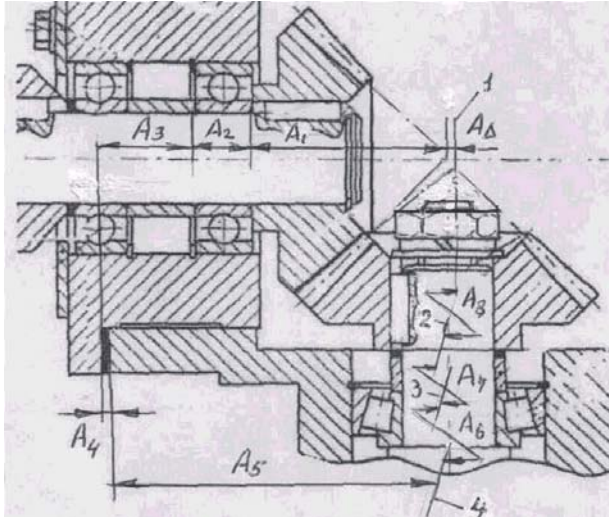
Схема размерной цепи A_{Δ} , определяющей совпадение вершин делительных конусов по горизонтали: 1 – ось делительного конуса; 2 – ось базового отверстия колеса; 3 – ось опорной ступени вала; 4 – ось отверстия в корпусе под подшипник
